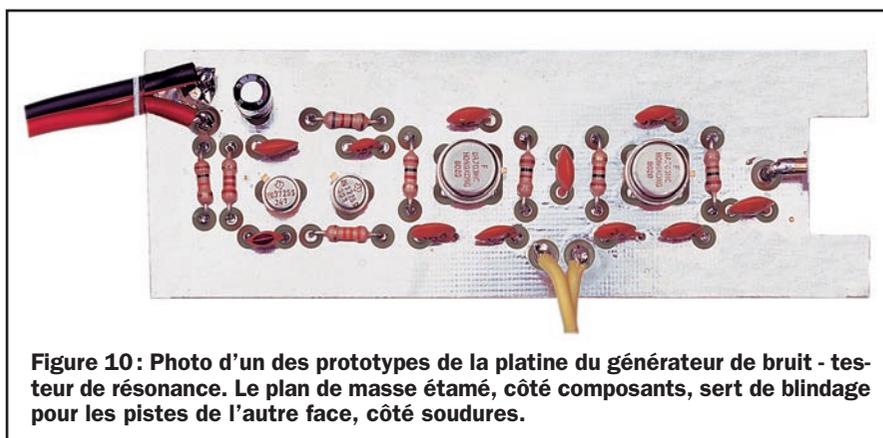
Photo d'un des prototypes de la platine du générateur de bruit - testeur de résonance. Le plan de masse étamé, côté composants, sert de blindage pour les pistes de l'autre face, côté soudures.
